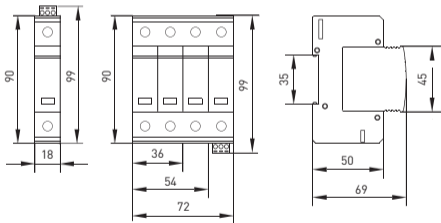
Габаритные размеры УЗИП класса T1+T2
